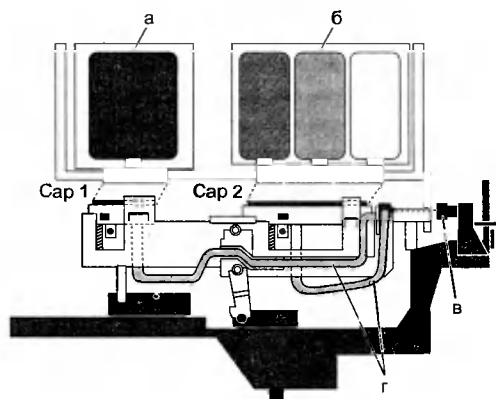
Прикрывающий механизм. а — черный чернильный картридж, б — цветной чернильный картридж, в — воздушный клапан, г — воздуховод
